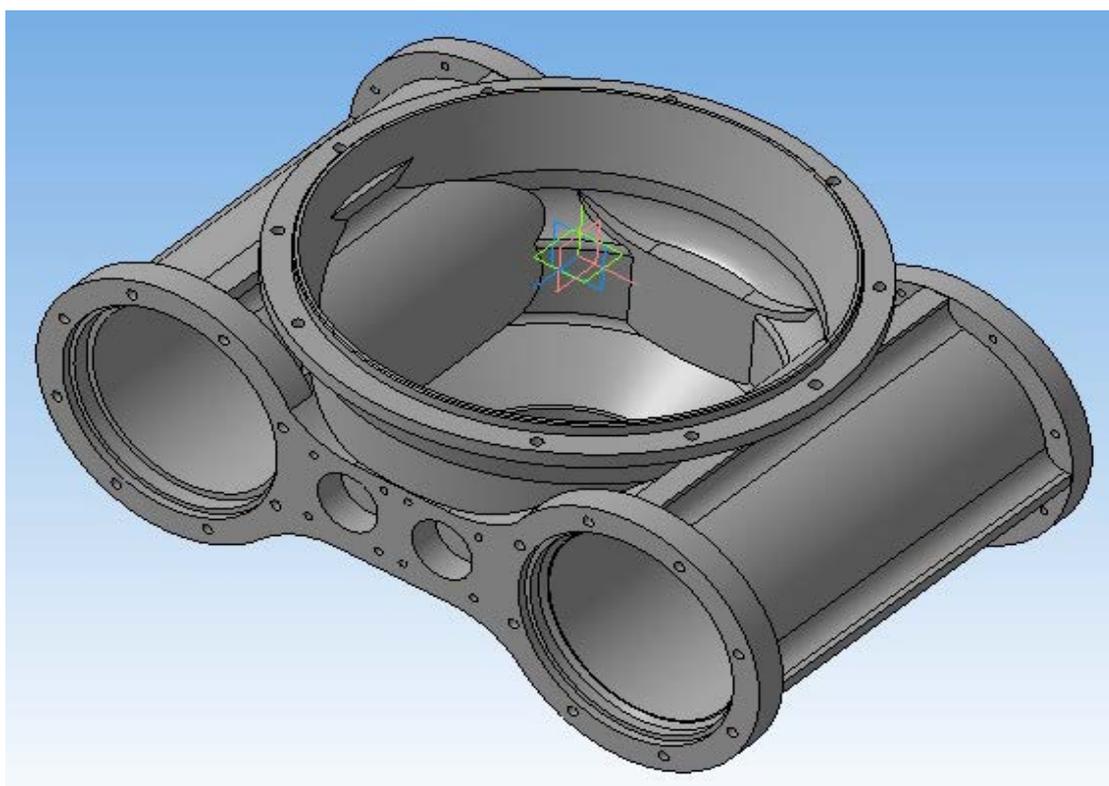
3D модель детали «Корпус привода вентилятора»
